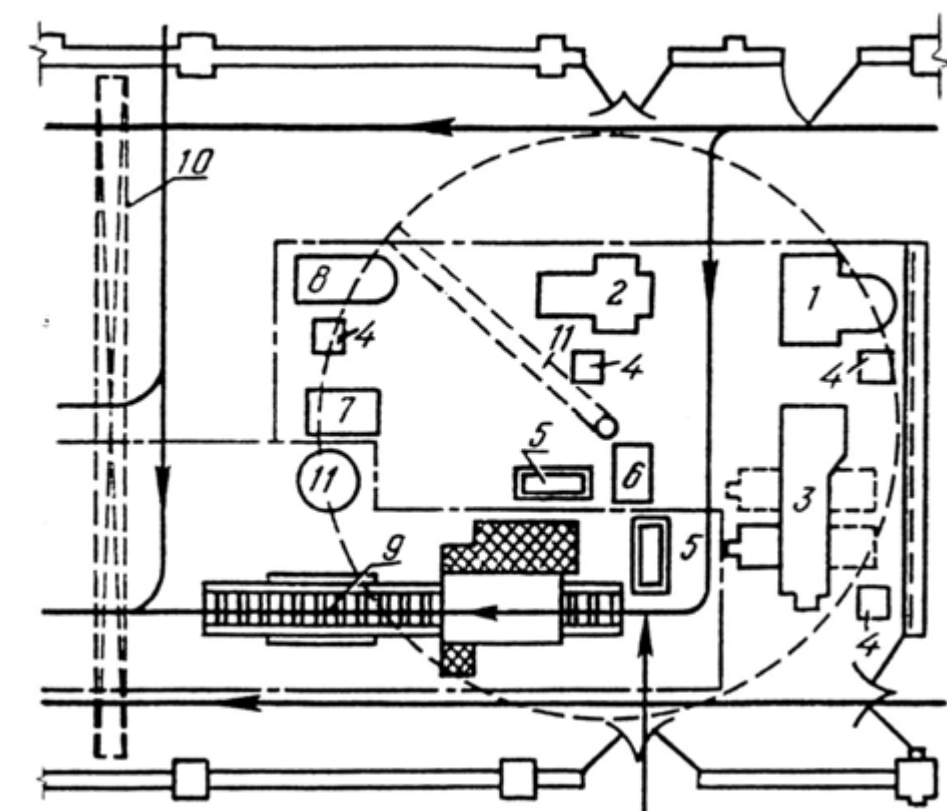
Робоче місце з відновлення корпусних деталей: 1 - вертикально-розточний верстат, 2 - хонінгувальний верстат, 3 - горизонтально-розточний верстат, 4 - тумбочка для інструменту; 5 - підставка для блоків циліндрів; 6 - гідравлічний прес; 7 - пересувний обдирково-шліфувальний верстат з гнучким валом, 8 - радіально-свердильний верстат, 9 - рольганг; 10 - електрифікована кран-балка; 11 - консольно-поворотний кран з електротельфером.
